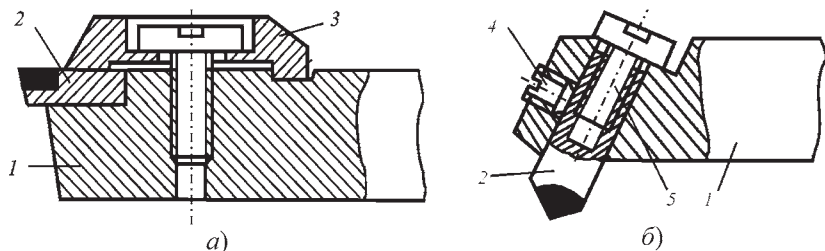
Резцы с механическим креплением вставок из СТМ прихватом сверху (а) и по боковой поверхности (б)
